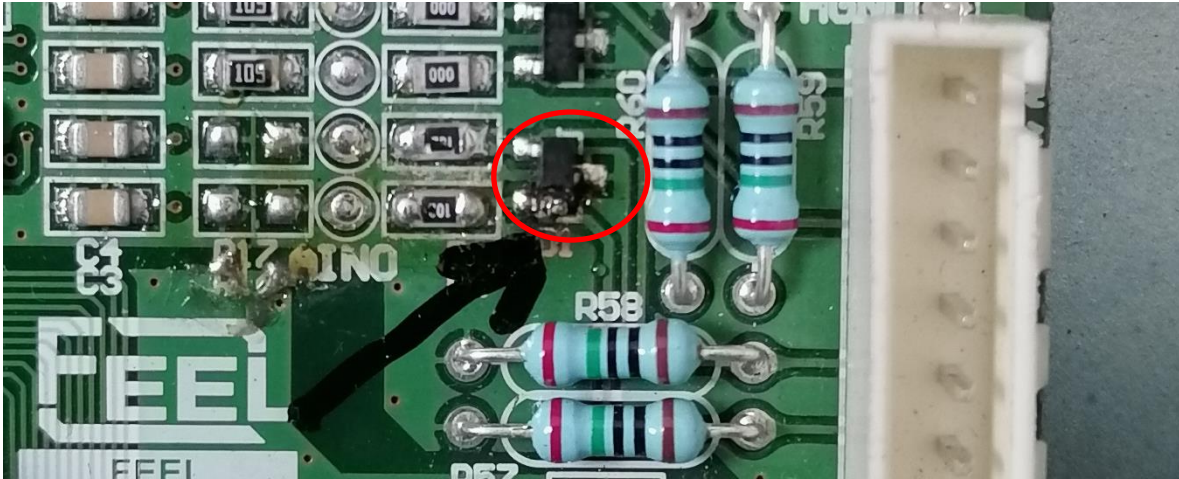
Ubicación de componente quemado en tarjeta pcb de equipo pressure.
